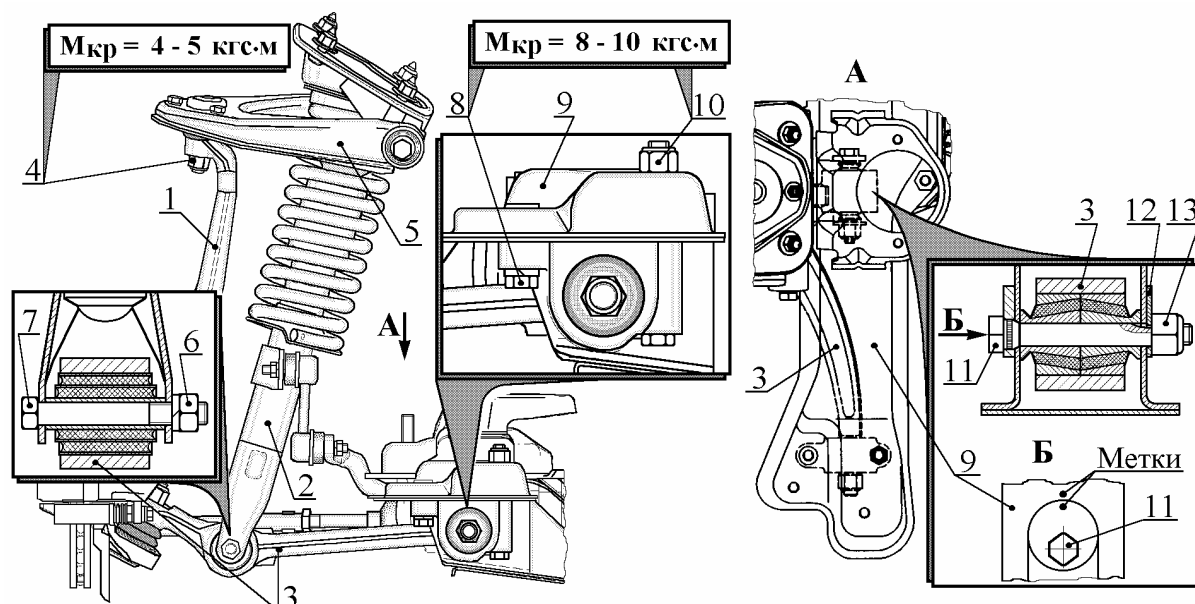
Установка поворотной стойки со ступицей, тормозом и нижним рычагом в сборе:
